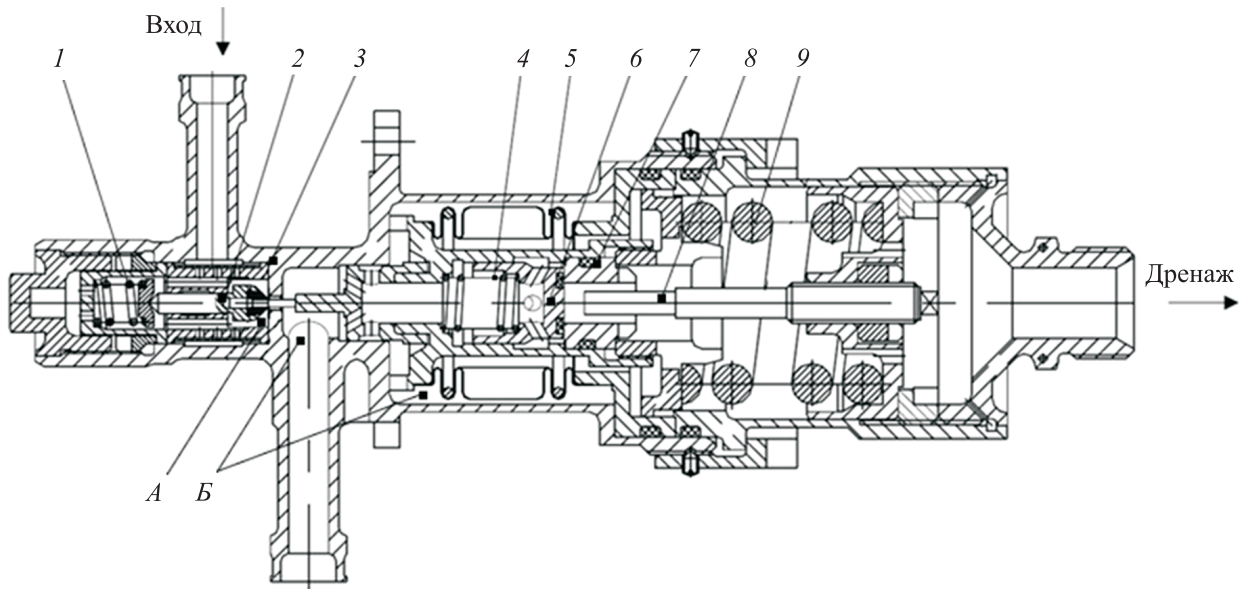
Конструктивная схема РДПД со встроенным предохранительным клапаном: 1 — пружина редукционного клапана; 2 — редукционный клапан; 3 — корпус; 4 — пружина предохранительного клапана; 5 — чувствительный элемент; 6 и 7 — предохранительный клапан и его седло; 8 — шток; 9 — задатчик давления (пружина РДПД); А и Б — полость высокого и низкого давления
